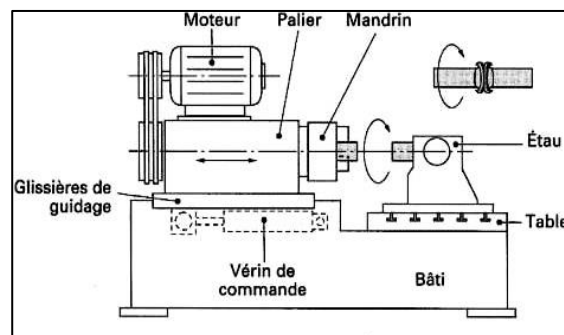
Exemple d'une machine de soudage par friction [5].
